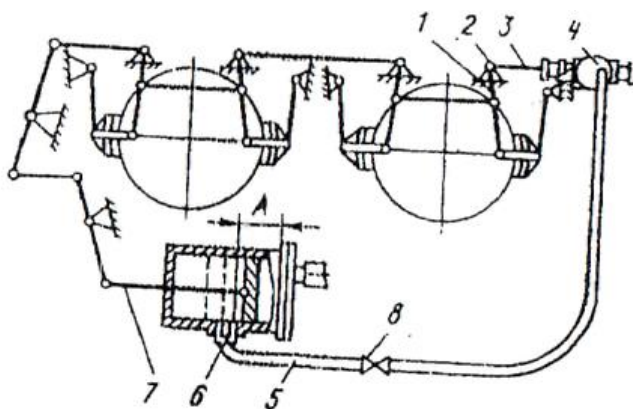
Схема действия авторежима: 1, 2 – шарнирные соединения; 3 – тяга; 4 – авторегулятор; 5 – патрубок; 6 – нипель тормозного цилиндра; 7 – шток; 8 – разобщительный кран
